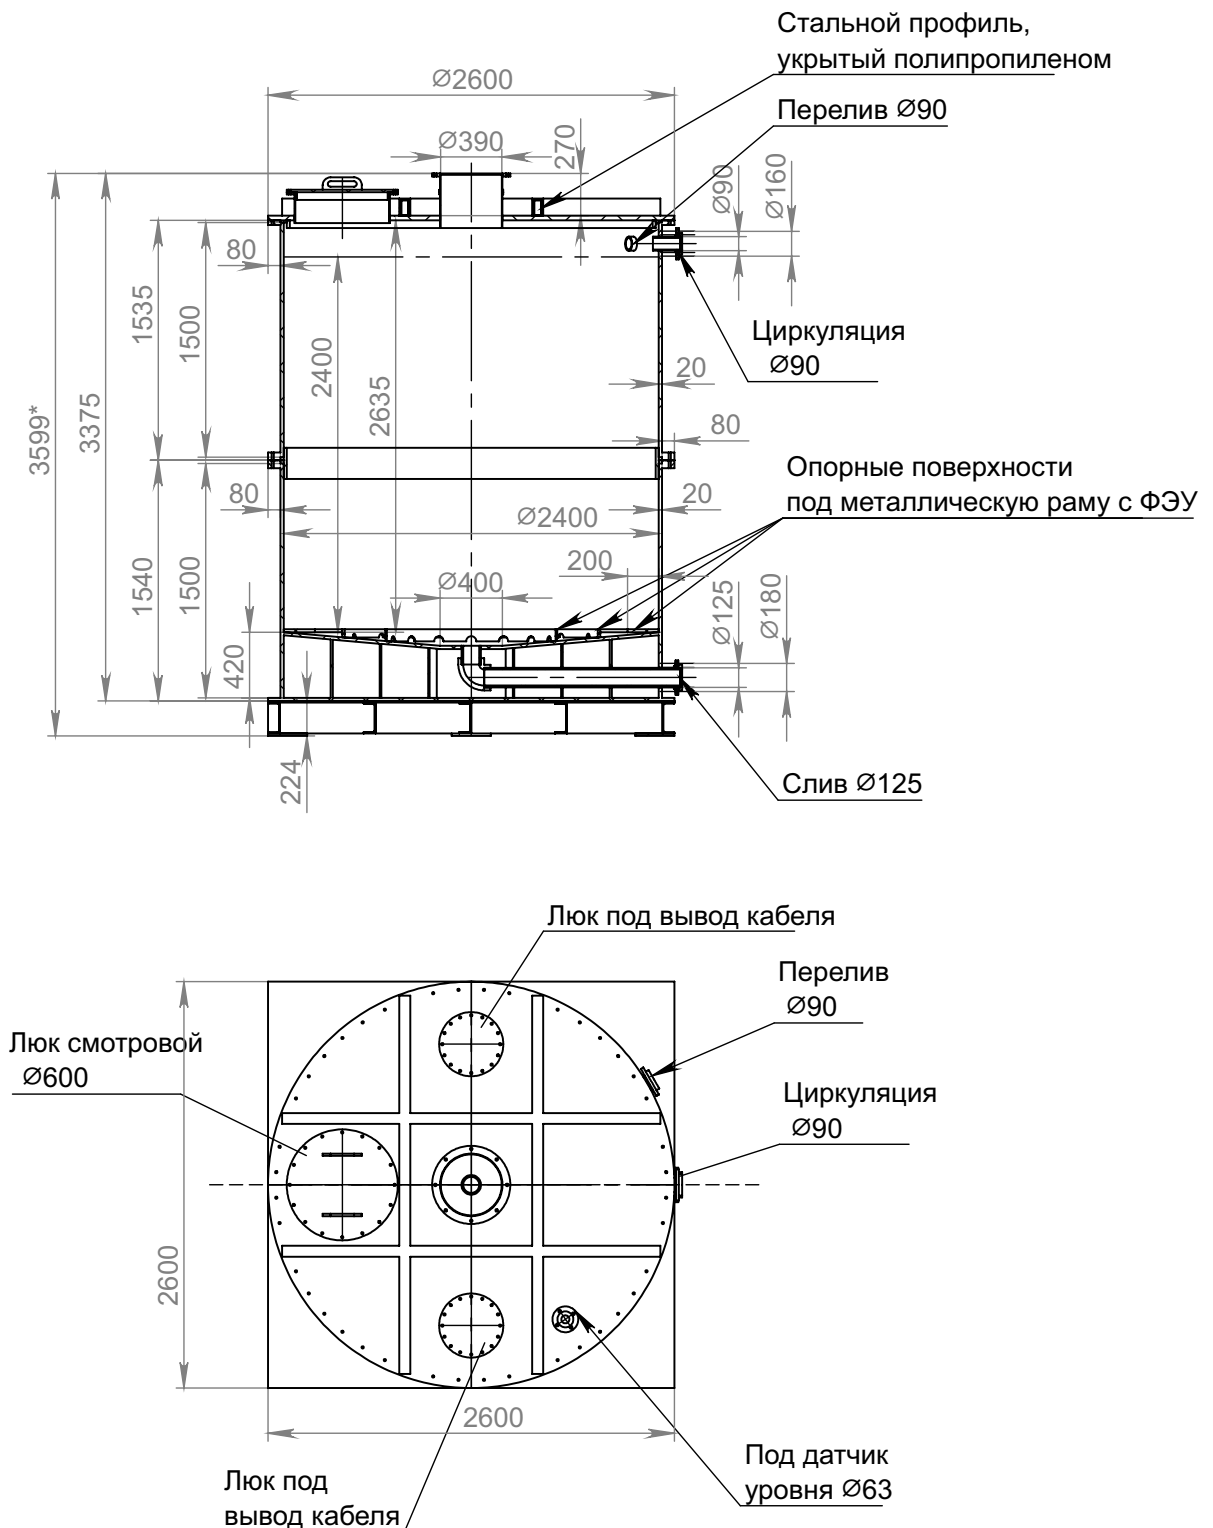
Чертёж водного резервуара. Вид сбоку и вид сверху.
